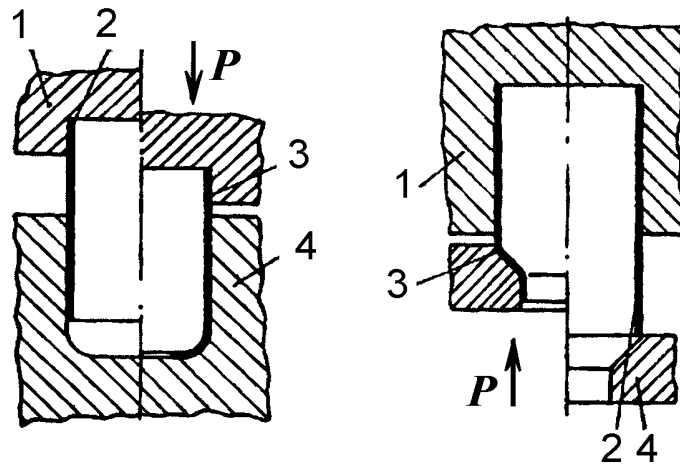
Схема одержання деталей із трубчастих заготовок обтисненням: 1 – контейнер; 2 – заготовка; 3 – деталь; 4 – матриця
